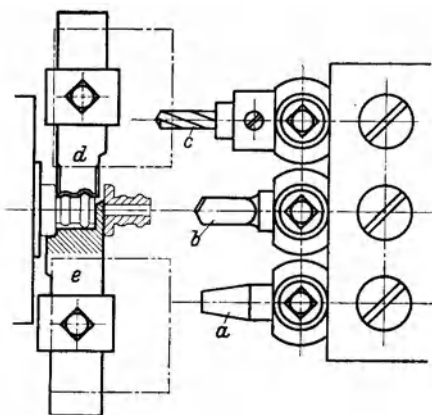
Bearbeitung eines Schlauchnippels aus Al-Legierung.
